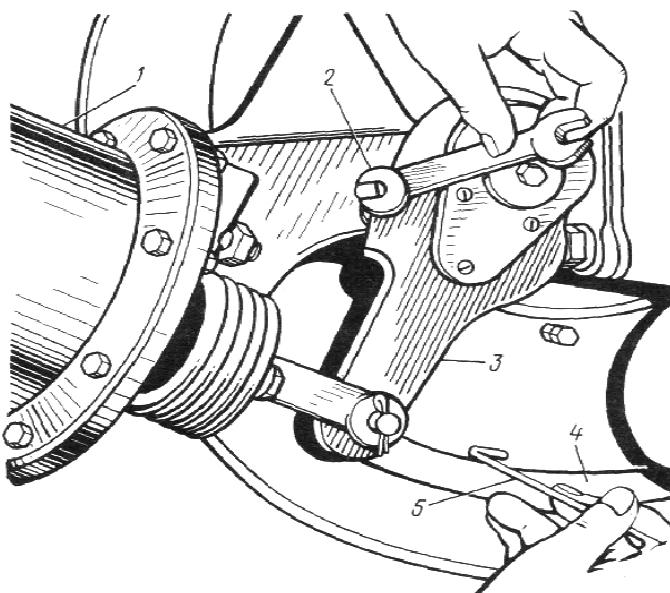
Проверка и регулировка колесных тормозных механизмов:
